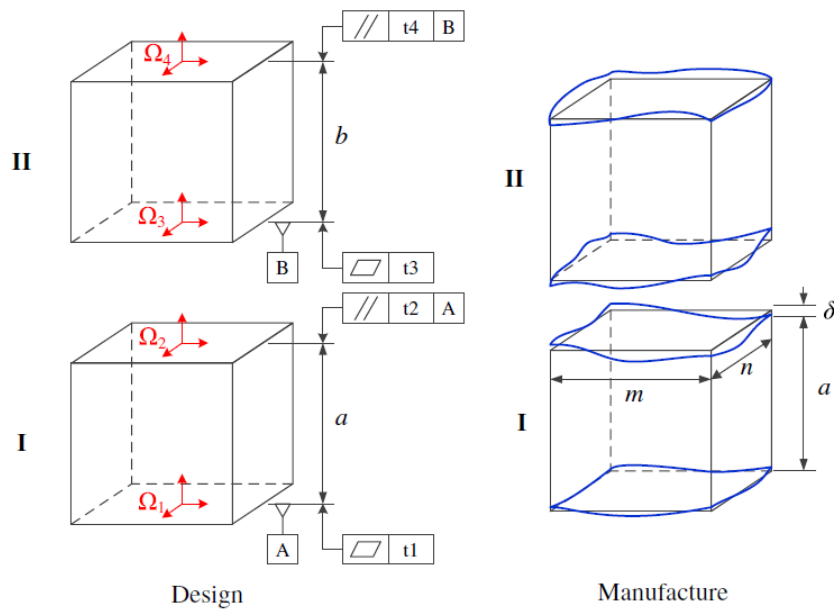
Étude de l'assemblage de deux pièces avec écarts de forme et déformation (Guo, et al., 2016)
